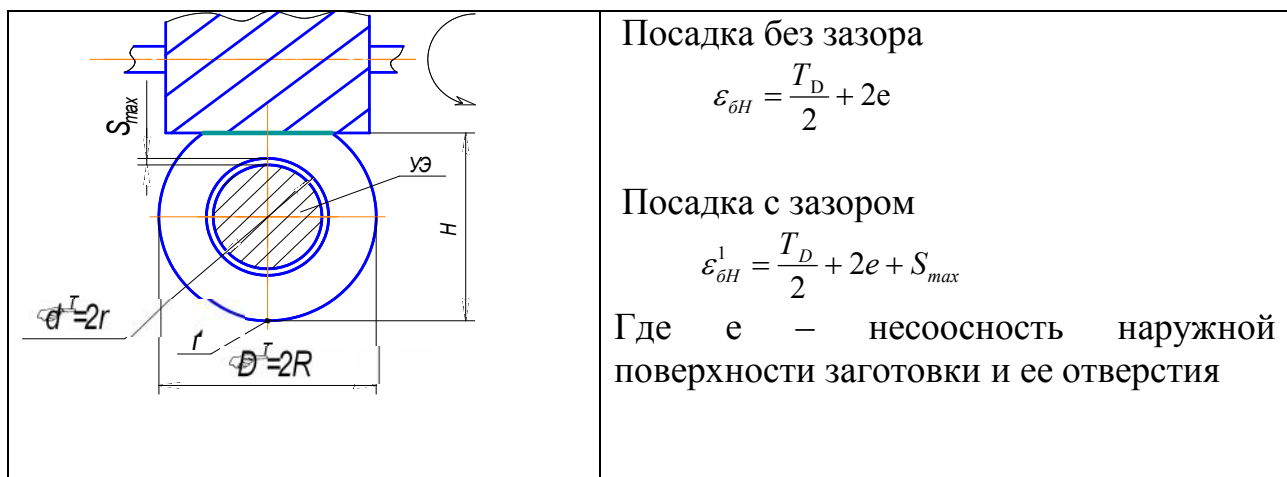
Схема для определения погрешности базирования размера H цилиндрической заготовки, установленной на горизонтальный установочный палец
